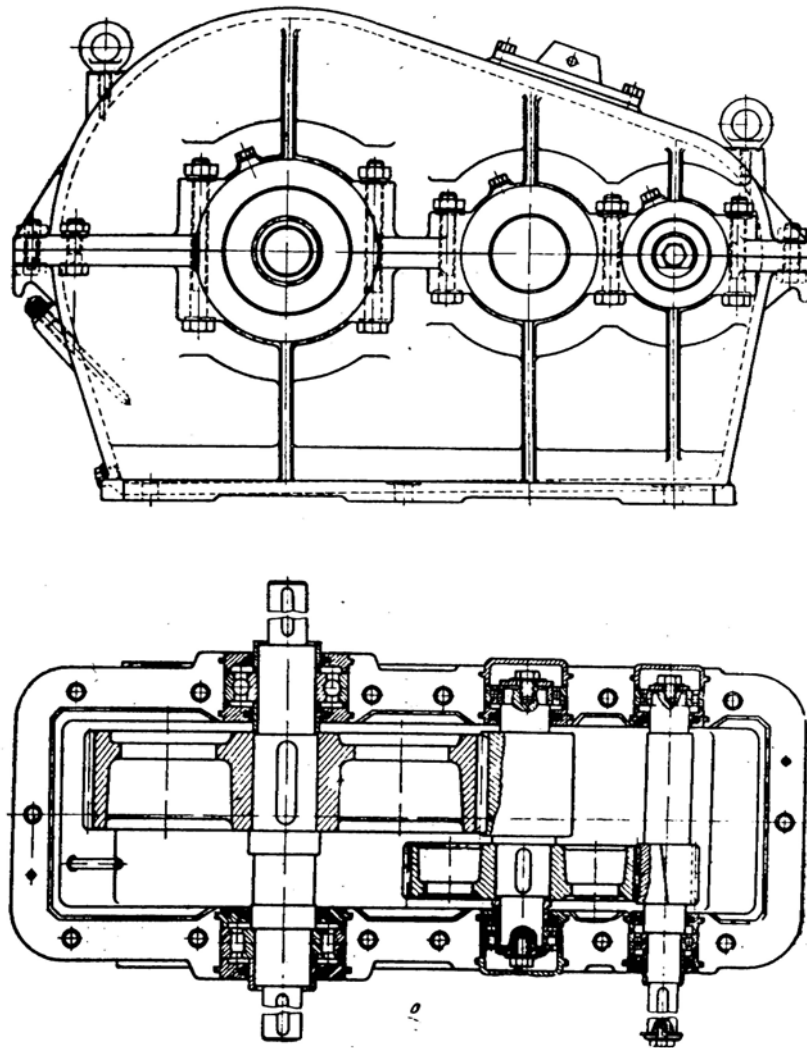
Двухступенчатый редуктор с цилиндрическими зубчатыми колесами
